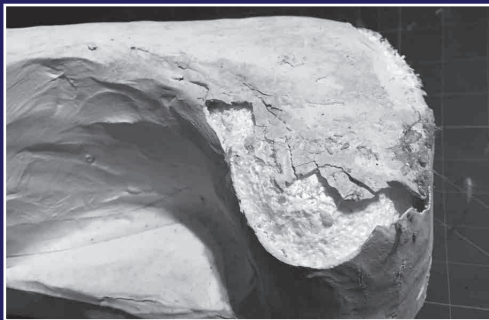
Molde afectado por la incorrecta aplicación de desmoldante.
